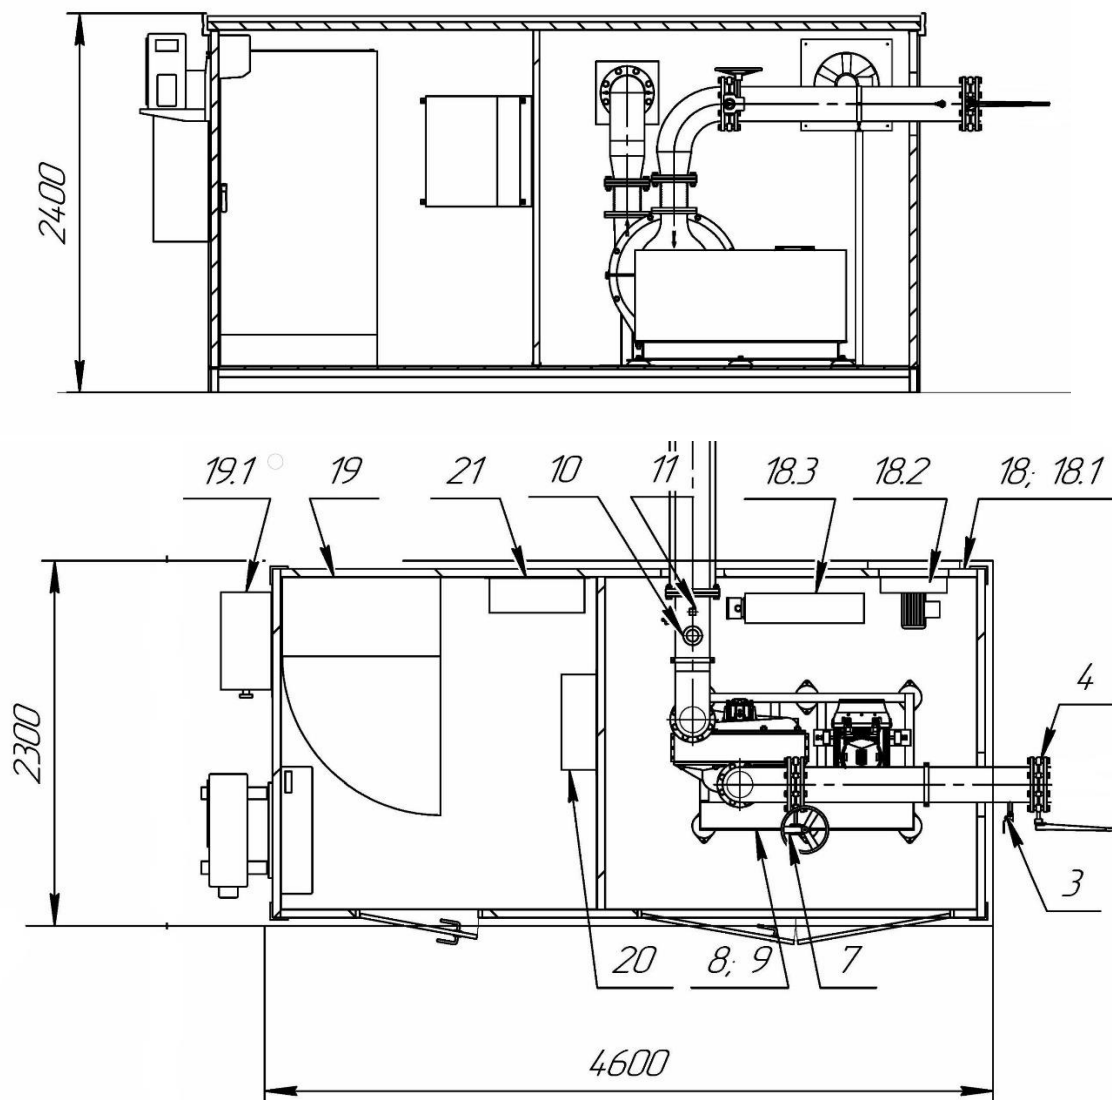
габаритные размеры и основные компоненты (3 - Точка отбора проб с шаровым краном, Dn 1/2"; 4 - Затвор поворотный дисковый, Dn 200; 7 - Затвор поворотный дисковый с приводом, Dn 200; 8 - Антивибрационное соединение; 9 - Компрессор-воздуходувка 1500 м³/час, 30 кВт; 10 - Датчик температуры; 11 - Датчик давления, диапазон 0/+400 мбар; 18 – Контейнер; 18.1 - Датчик утечки газа; 18.2 – Вытяжка; 18.3 - Радиатор отопления; 19 - Панель управления; 19.1 - Внешний модуль панели управления; 20 - Система анализа биогаза).
